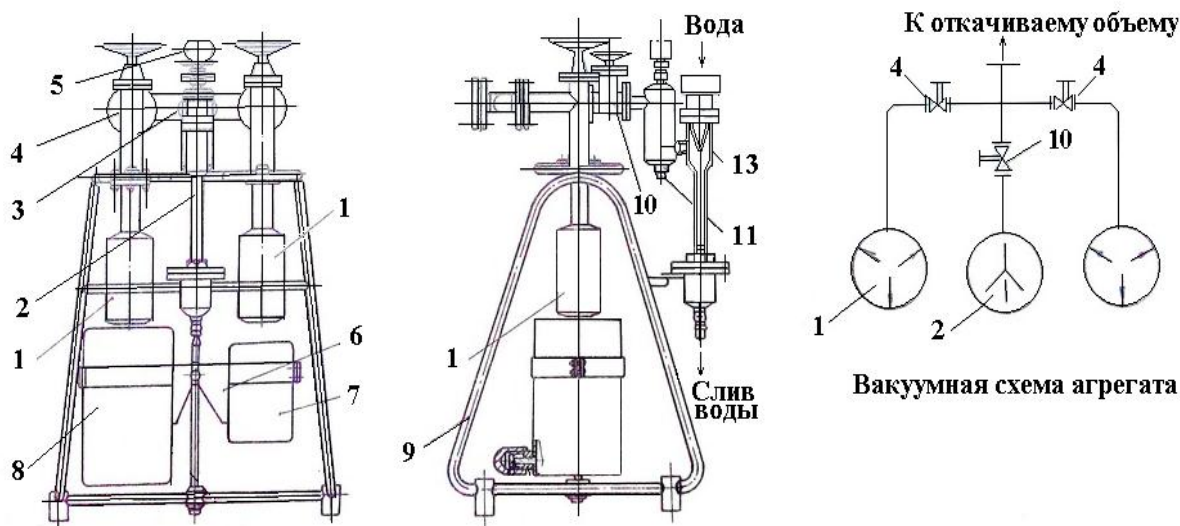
Схема агрегата ЦВА-1-2: 1 - цеолитовые вакуумные насосы ЦВН-1-2; 2 - водоструйный насос ВВН-2-2; 3 – трубопровод; 4 - вентили; 5 – вакуумметр; 6 - поддерживающая стойка с поворотной траверсой; 7 – электронагреватель; 8 - сосуда Дьюара; 9 – рама; 10 – вентиль водоструйного насоса ВВН-2; 13 – корпус насоса ВВН-2 с соплом; 14 – штуцер
